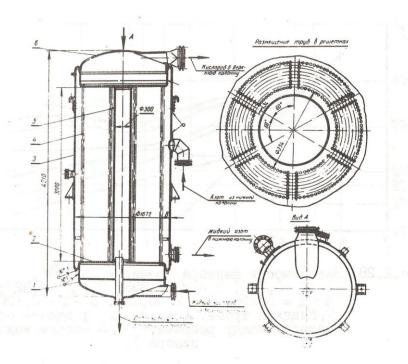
Фланцевый кожухотрубный конденсатор-испаритель с внутритрубным кип ением.
